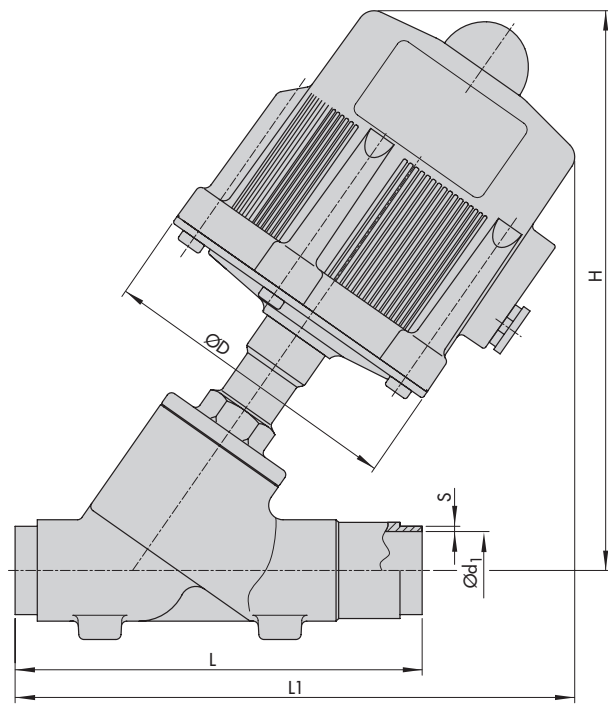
· Schrägsitzventil Typ 3353 mit Anschweißenden
